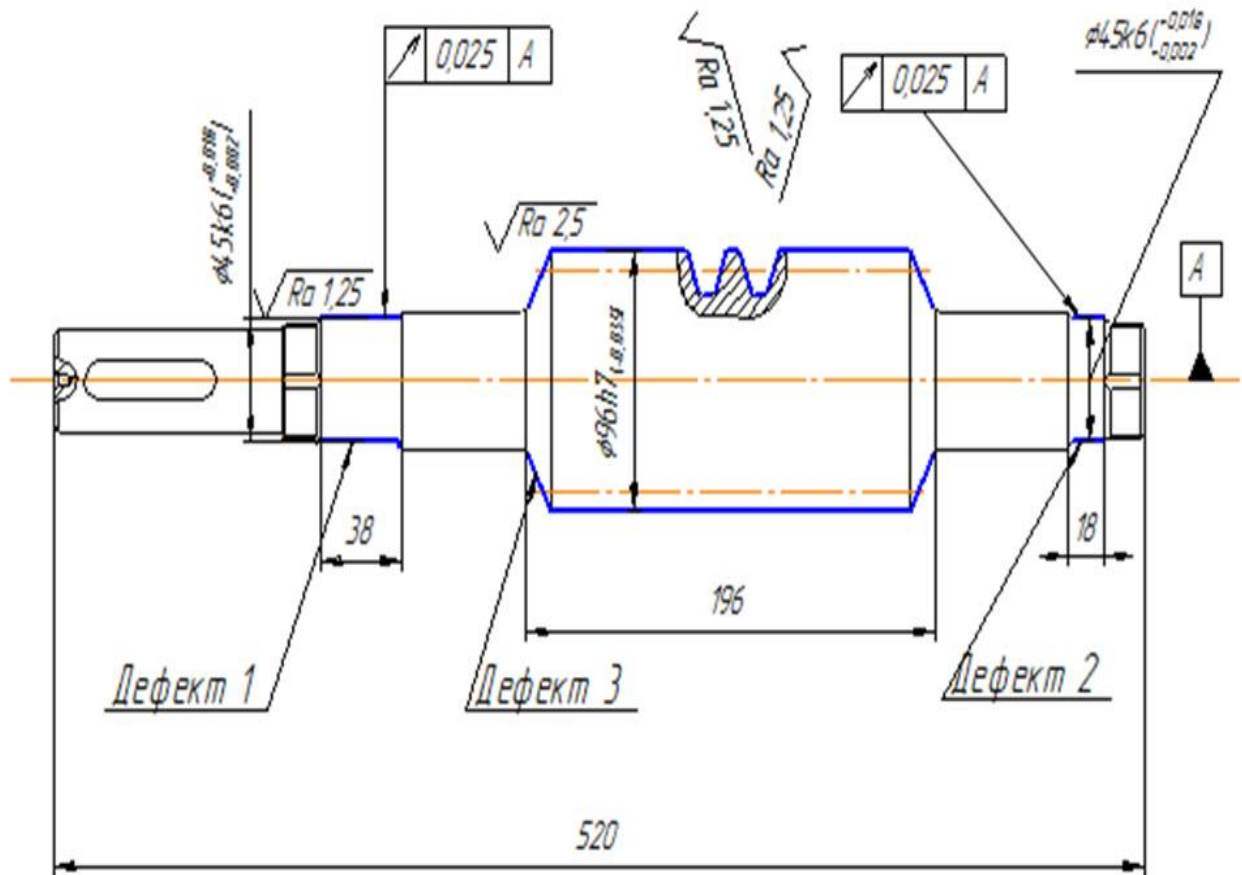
Ремонтне креслення вала черв'ячного редуктора РЧН-180М
